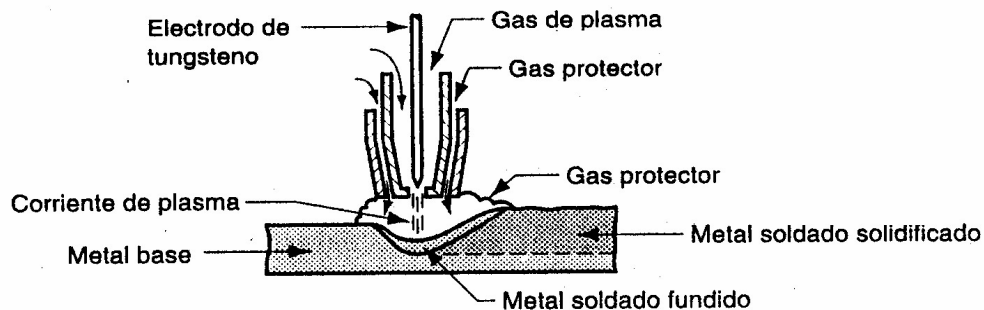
Soldadura de arco de plasma (PAW)
